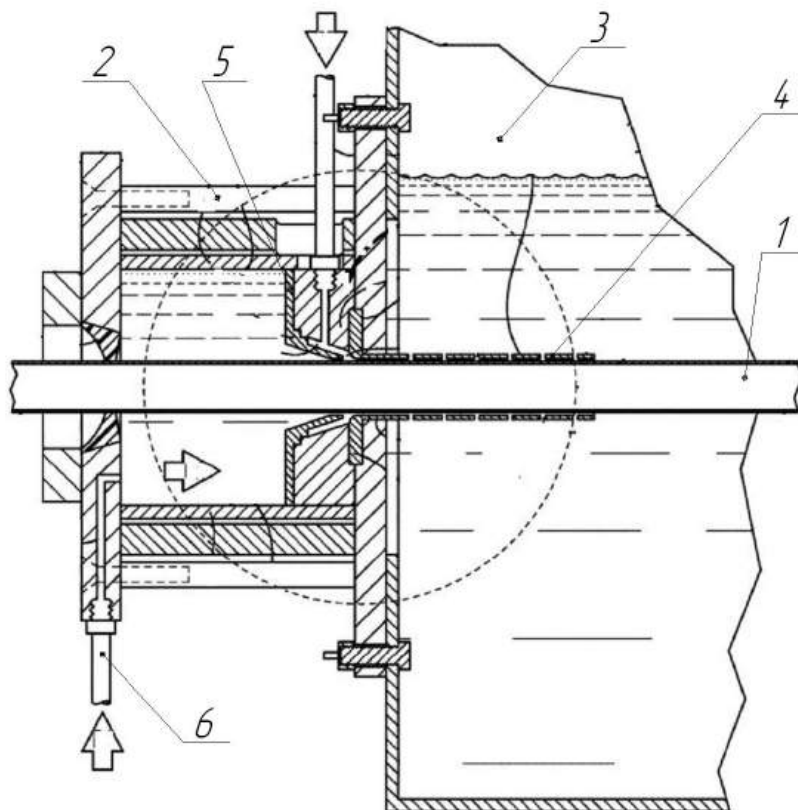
Наборний калібрувальний пристрій [41]
